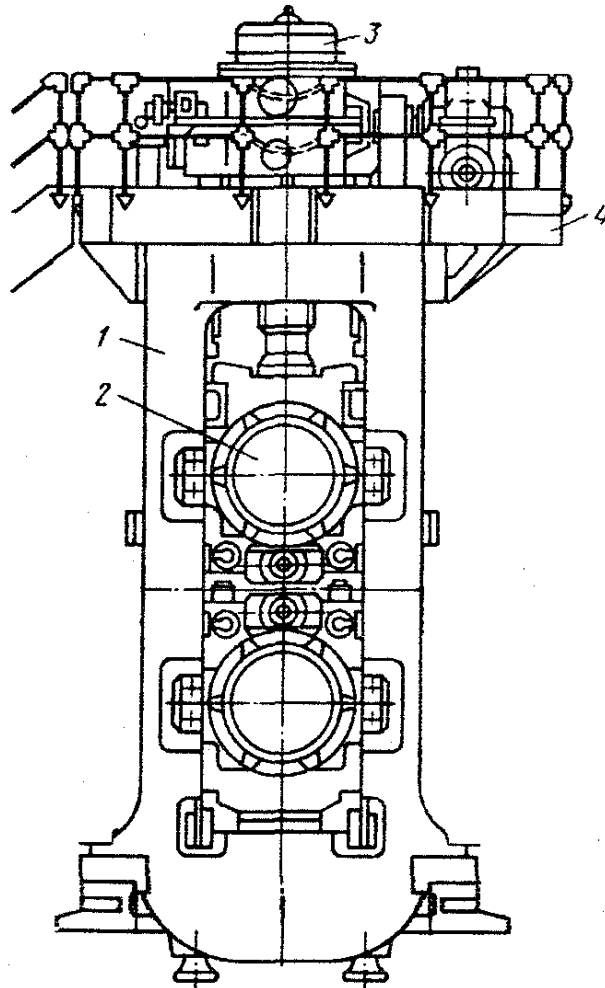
Загальний вид робочої кліті прокатного стана
